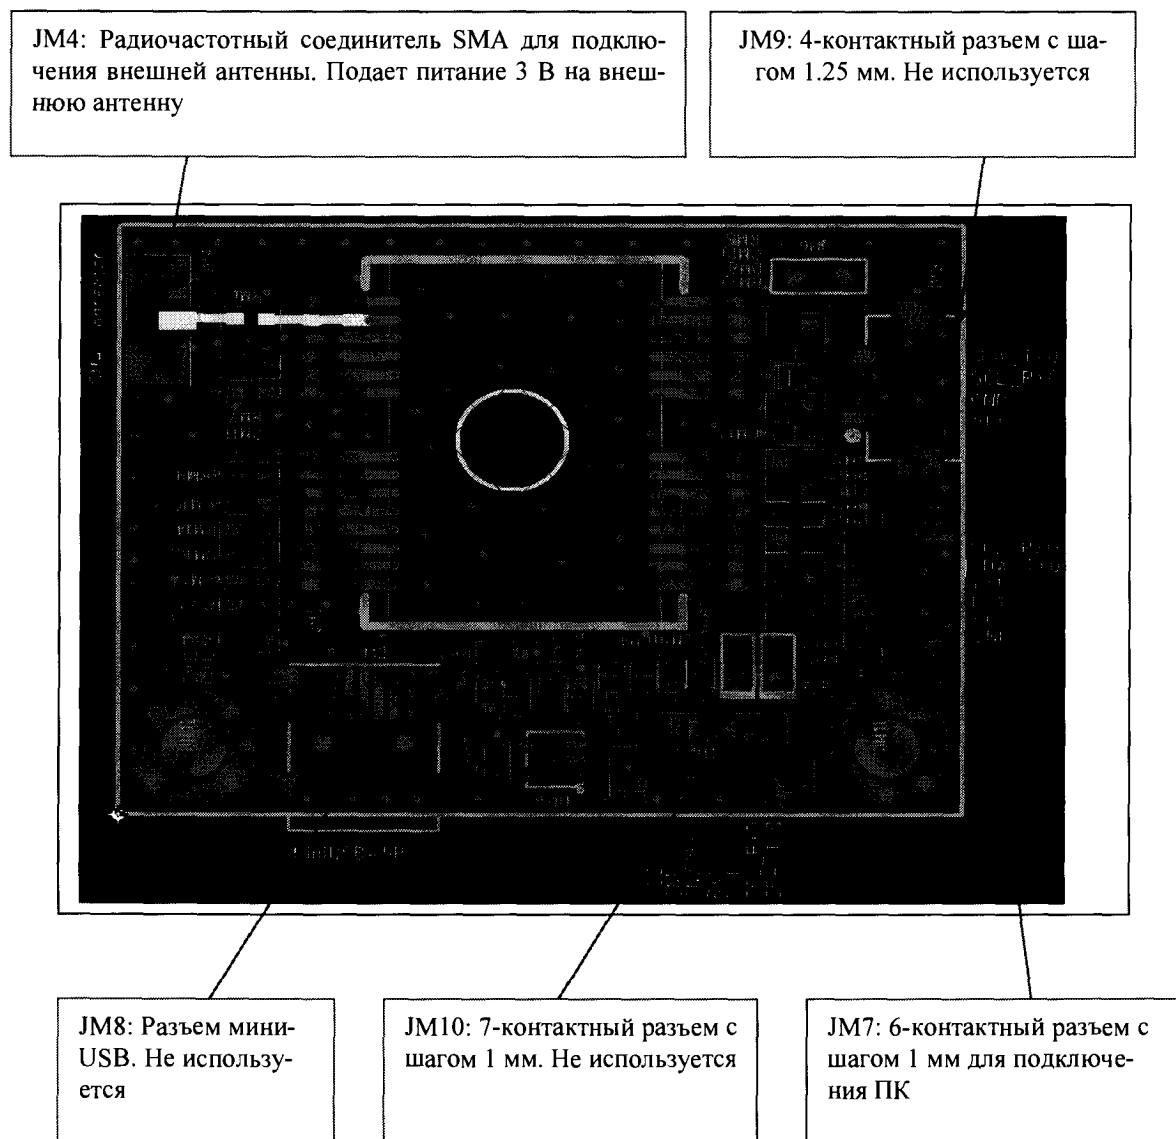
Внешний вид и назначение разъемов изделий MGGS2217-01/02
